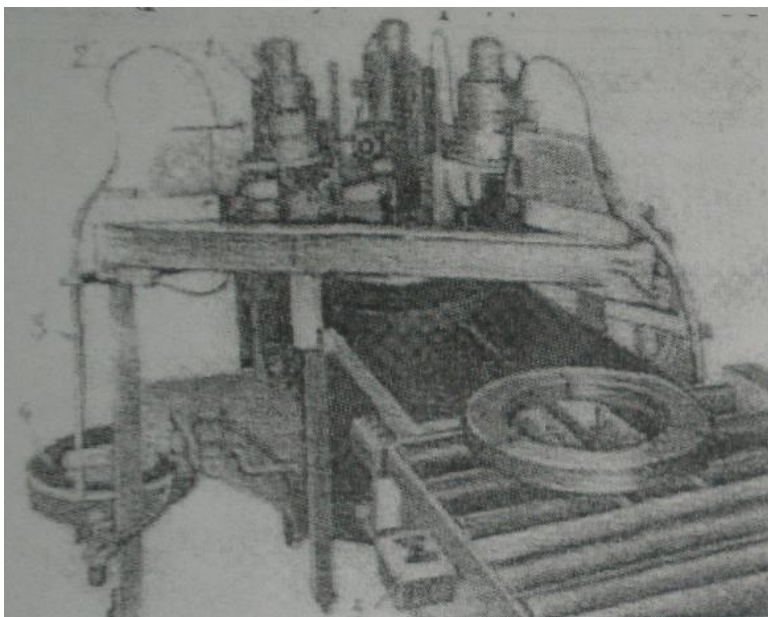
Автоматична установка для трьохпозиційної обв'язки
